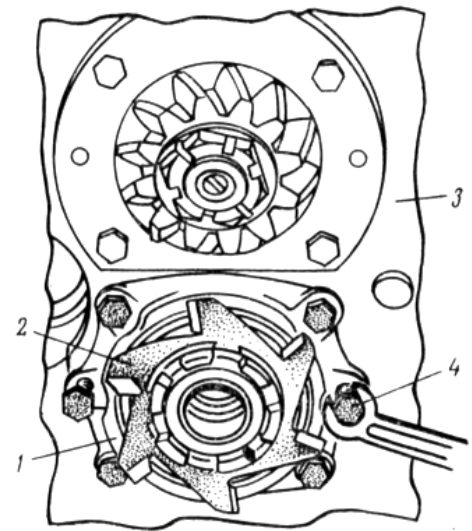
Випресування стакана підшипника ведучої шестерні II ступені редуктора: 1- стакан; 2- крильчатка; 3- корпус коробки передач; 4- технологічний болт.
